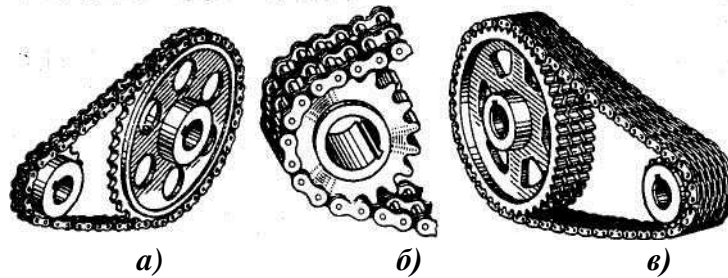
Типы цепных передач: *а* — с роликовой цепью; *б* — с втулочной цепью; *в* — с зубчатой цепью
